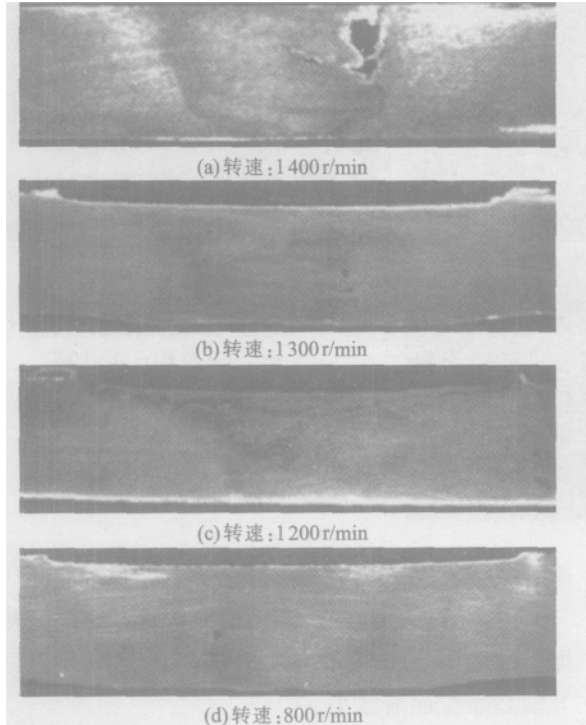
焊速为20mm/min时不同转速速度下的焊缝截面形貌
